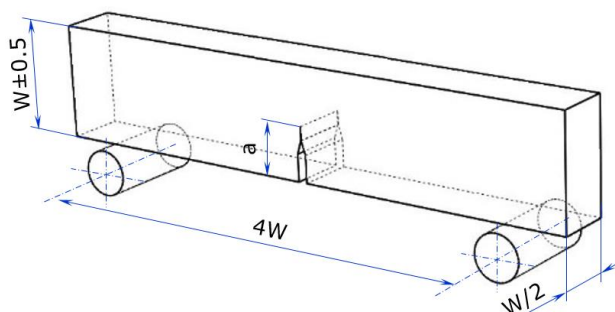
Geometria și dimensiunile epruvetei SENB printate 3D
